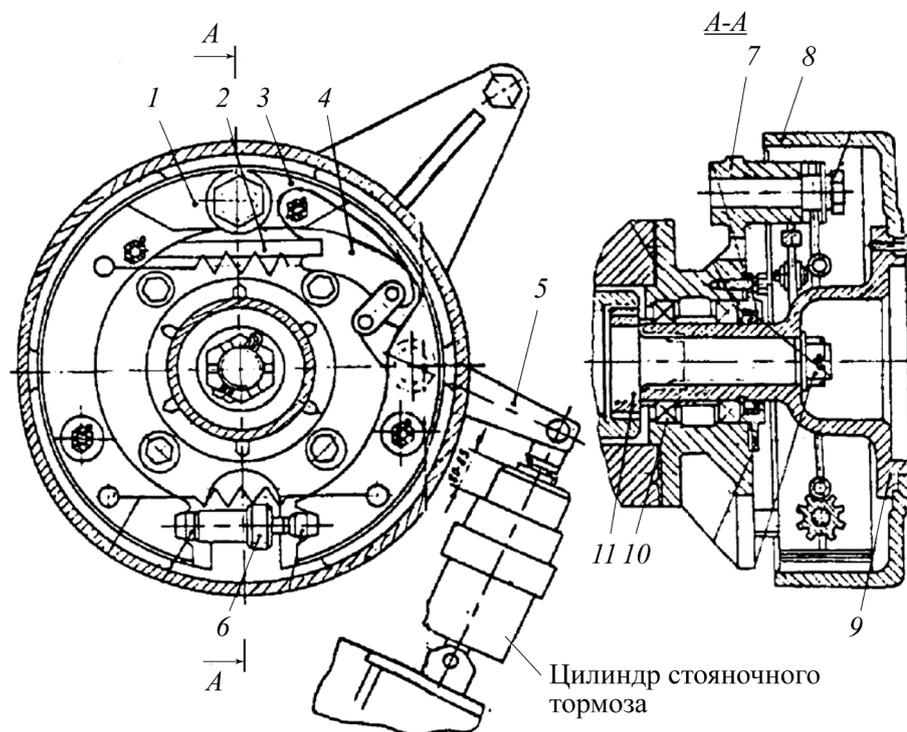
Стояночный тормоз самоходного вагона: *1, 3* – колодки тормозные; *2* – штанга; *4, 5* – рычаги; *6* – звездочка регулировочная; *7* – суппорт; *8* – барабан; *9* – ступица; *10* – подшипник; *11* – вал-шестерня
